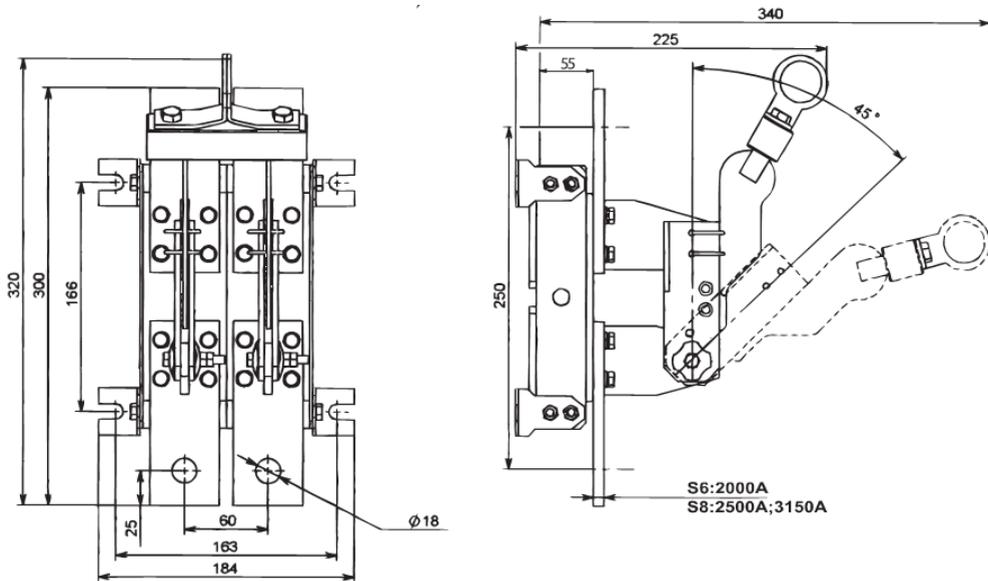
Разъединитель РЕ19 однополюсный
